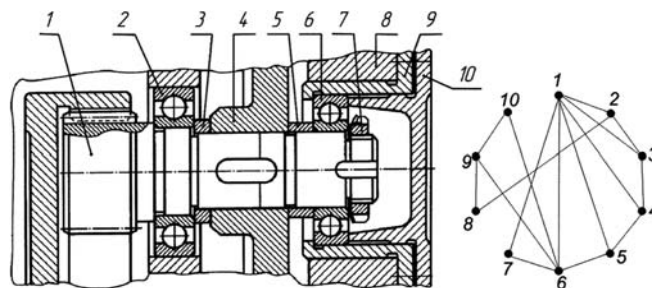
Промежуточный вал цилиндрического редуктора внутреннего зацепления
